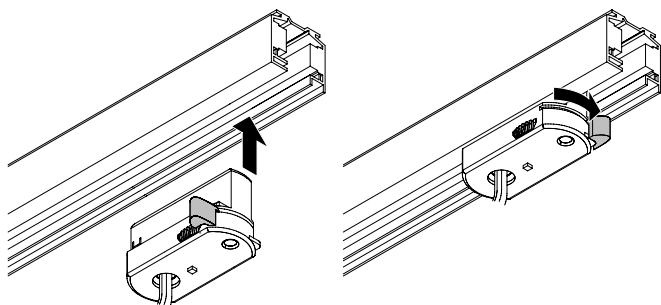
Enganche del adaptador en la canaleta eléctrica
